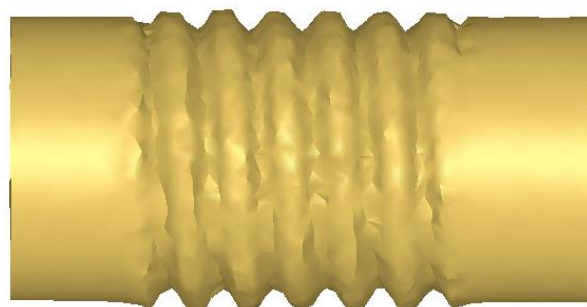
Общий вид резьбы, накатанной на заготовке после 4-х проходов РКУП
